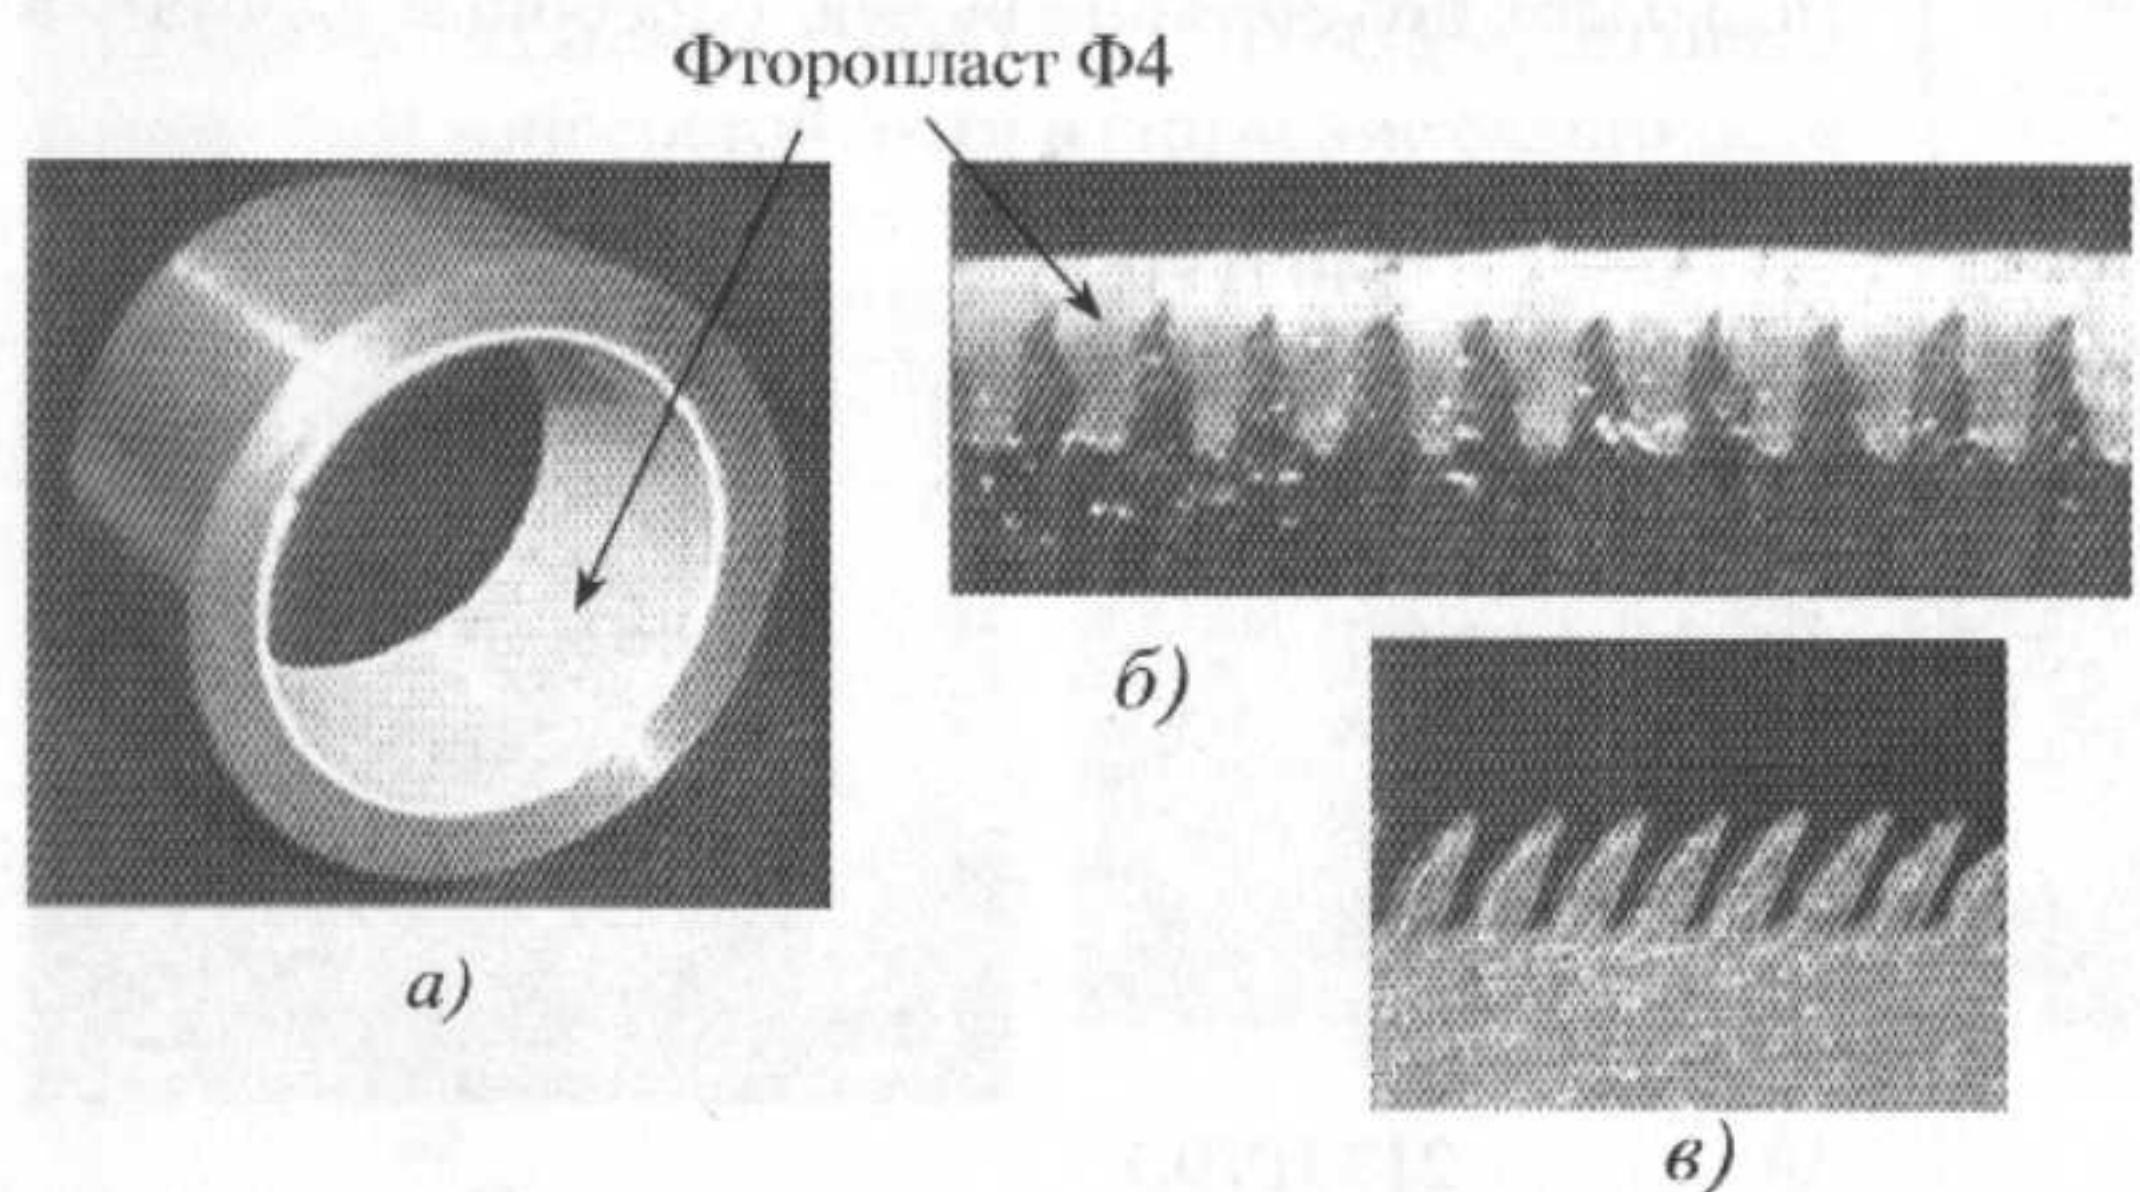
Фторопластовая (Ф4) лента, запрессованная во внутреннюю поверхность стальной (12Х18Н10Т) подшипниковой втулки (а, б), и поверхность фторопласта (Ф4), подготовленная под склеивание с другими материалами (в)
